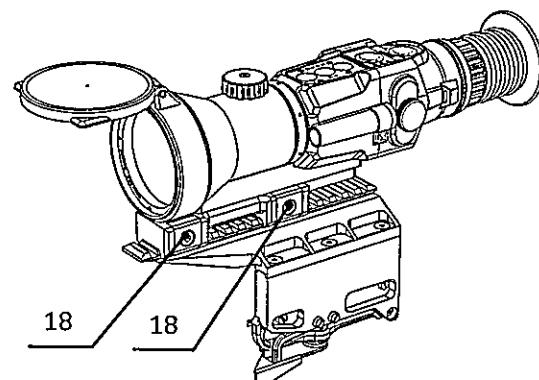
Изделие с боковой планкой крепления SMN WP-2525
